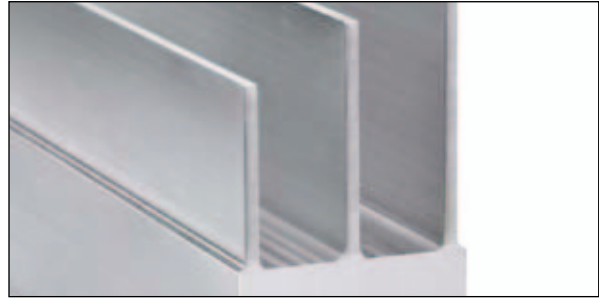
Pièce usinée de contrôle en aluminium aéronautique 7075
